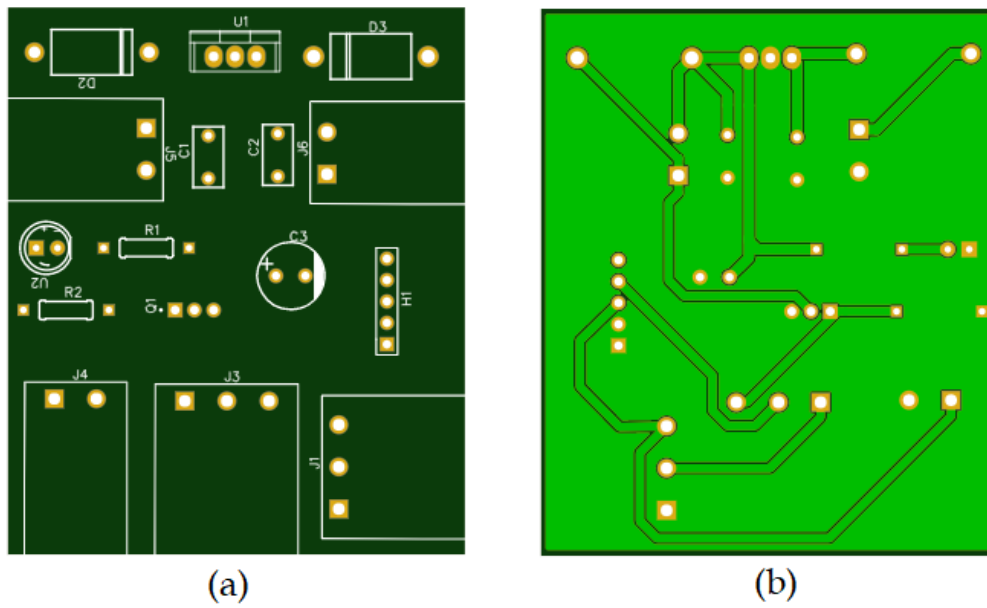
PCB projetada: (a) vista superior, (b) vista inferior
